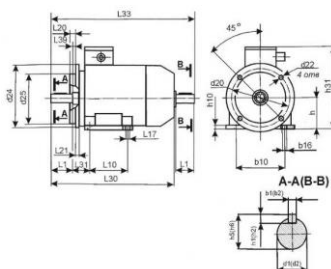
Габаритно-установочные и присоединительные размеры двигателя АИР56А4У3
